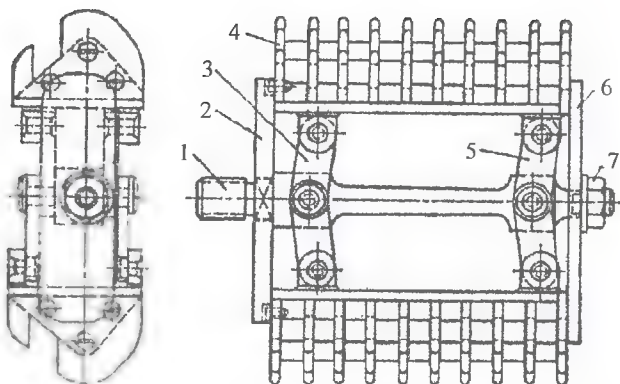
Шарнирный шаблон для намотки катушечных групп: 1 — вал шаблона; 2 — опорная планка; 3 — поворотная планка; 4 — колодки шаблона; 5 — поворотная планка; 6 — съемная планка; 7 — зажимная гайка на валу
